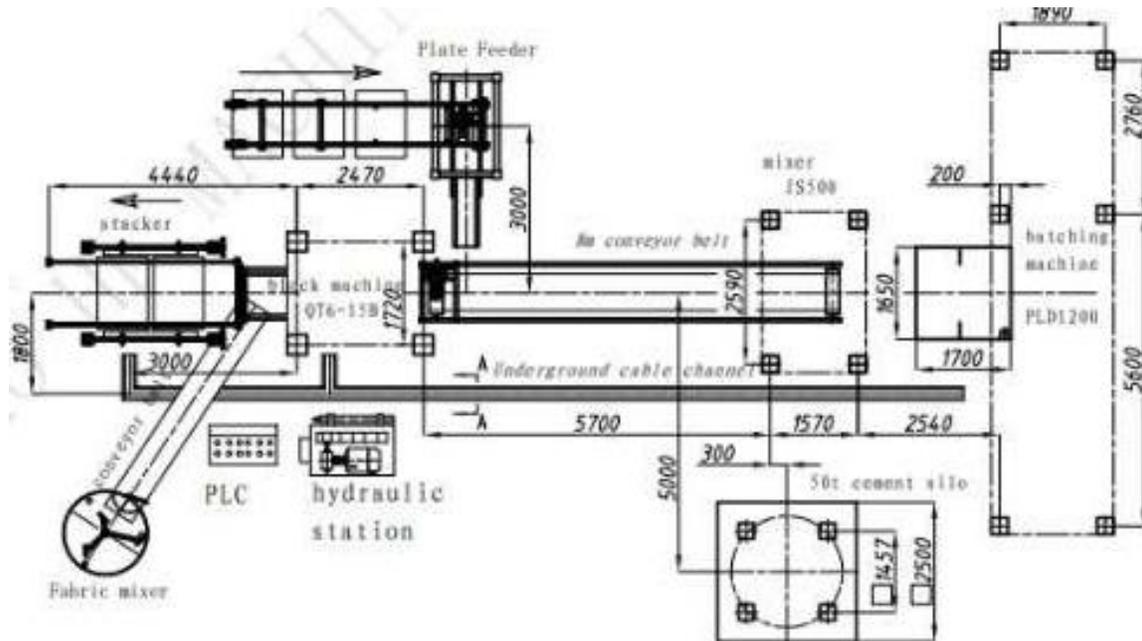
Distribución en planta de la máquina fabricadora de bloques.
